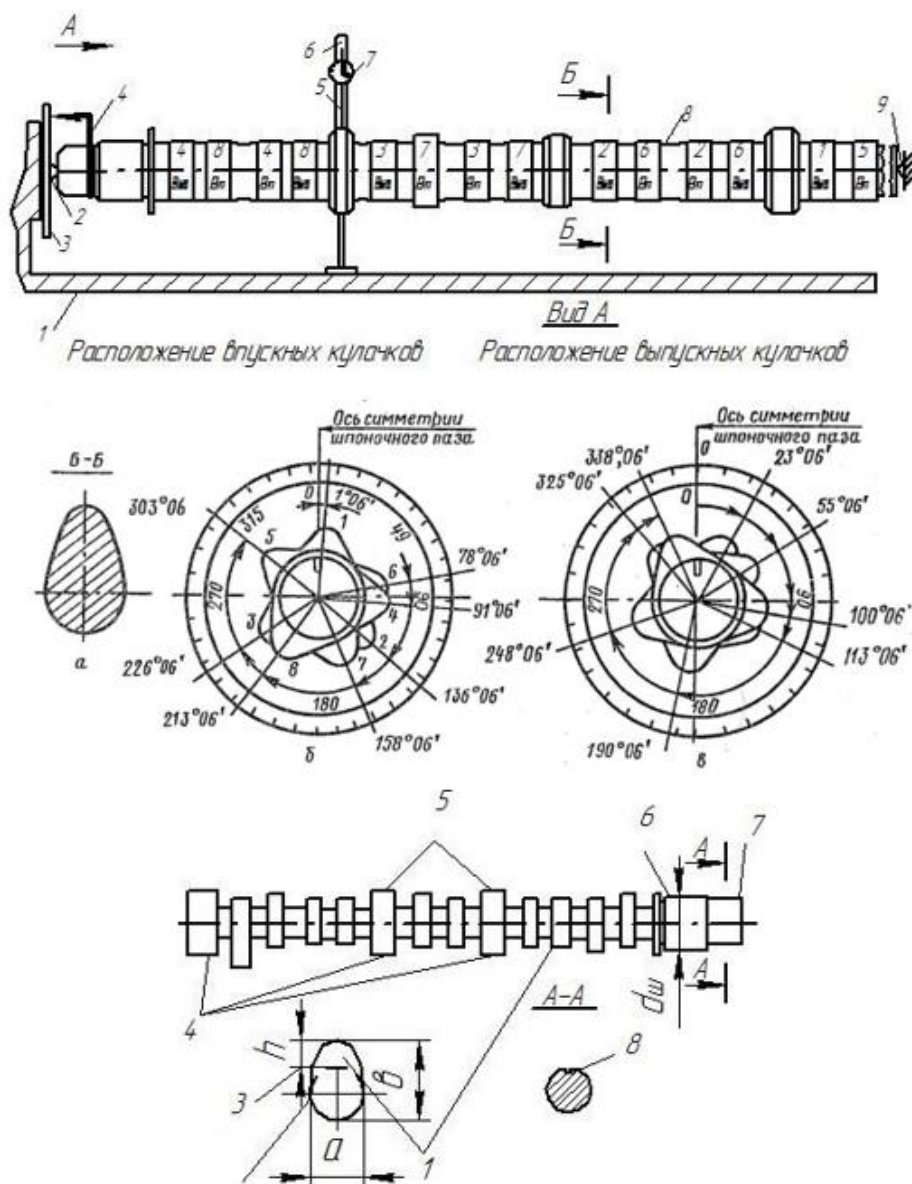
Приспособление для контроля профиля кулачков и опорных шеек распределительного вала:
